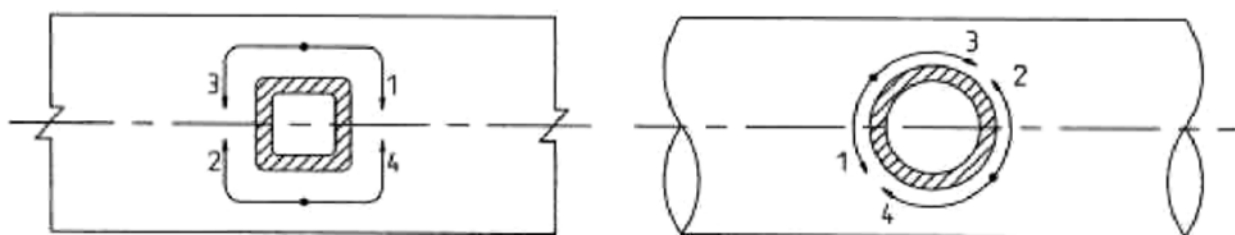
Начальные и конечные точки сварных швов и последовательность сварки.
